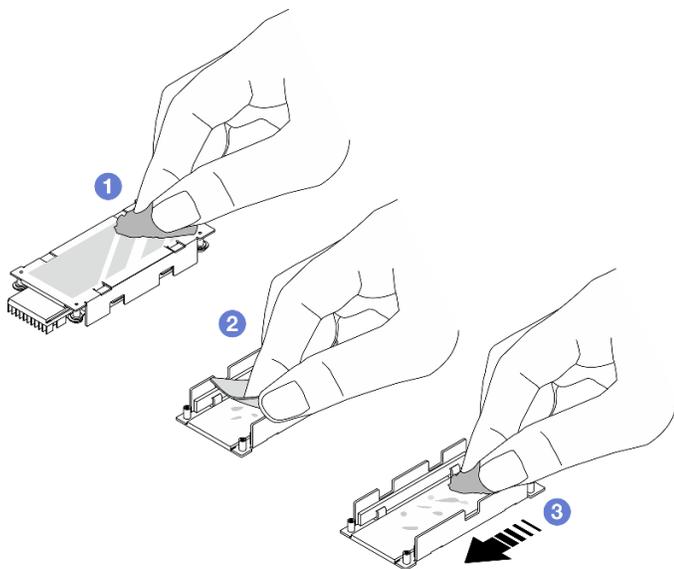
Nettoyage du dissipateur thermique et de la plaque inférieure
